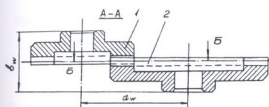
Торцовая зубчатая передача с круглыми зубчатыми колесами
